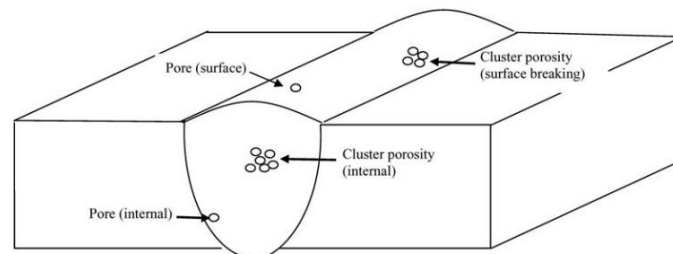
Porosidade em Cordões de Soldadura (Inclusões Gasosas) [9]
